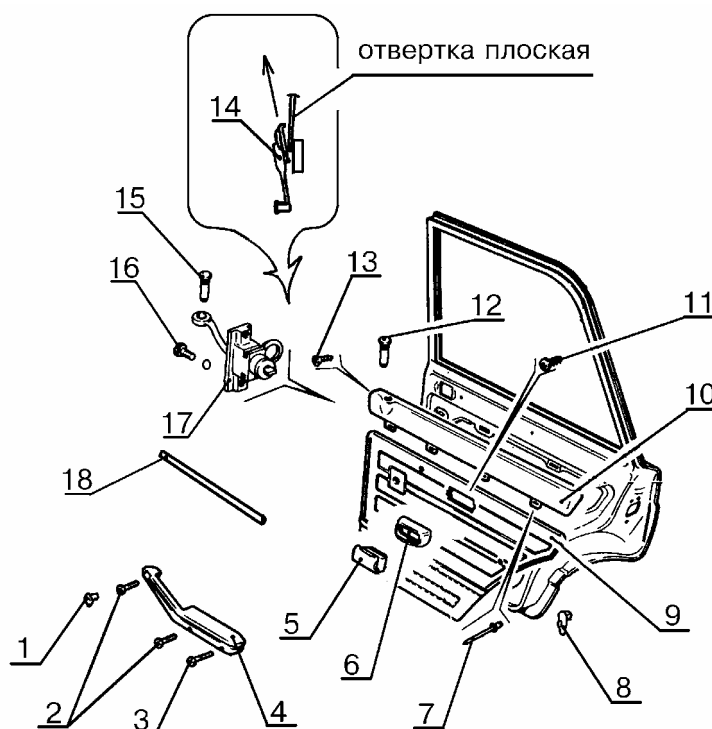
Дверь задняя ВАЗ-2105, 2107,2106:
